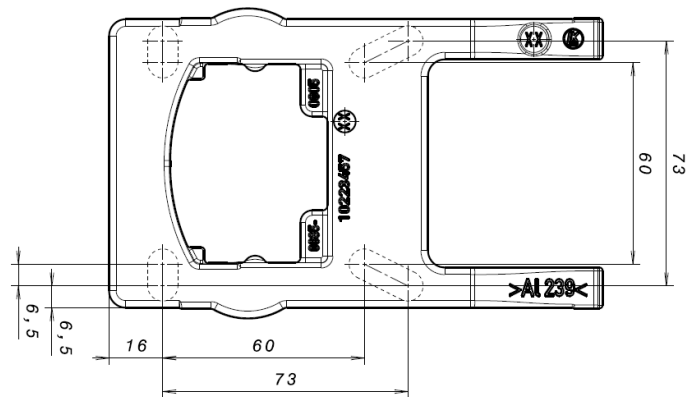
Bohrbild Standard-Adapterplatte BG A
